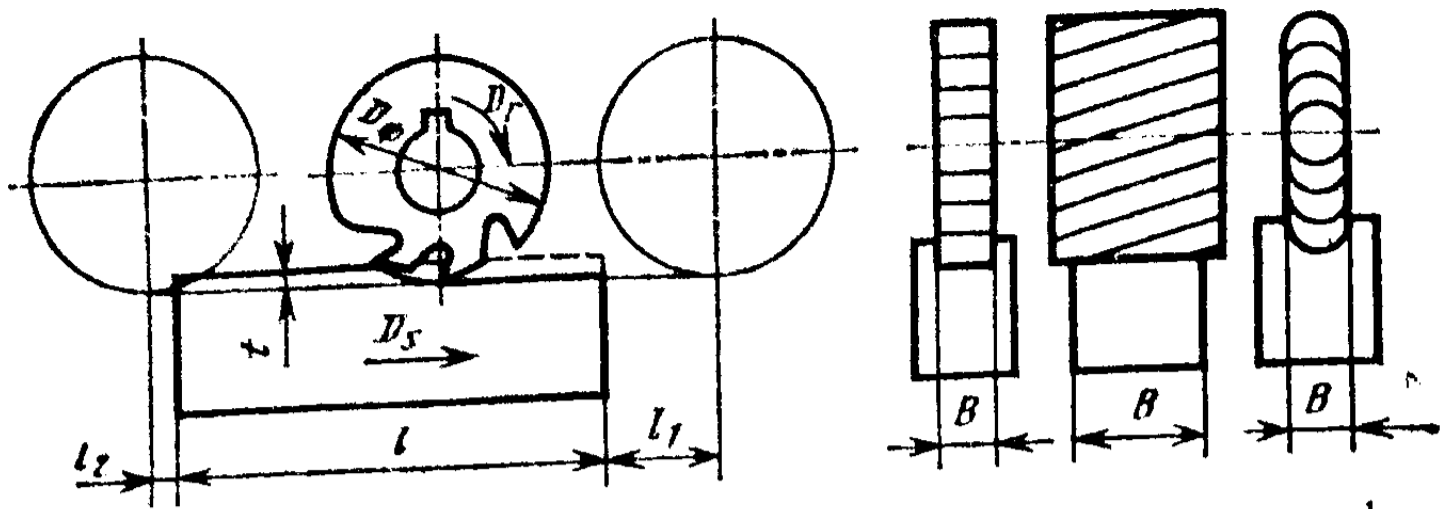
Путь, пройденный инструментом при фрезеровании фасонными, дисковыми и цилиндрическими фрезами
